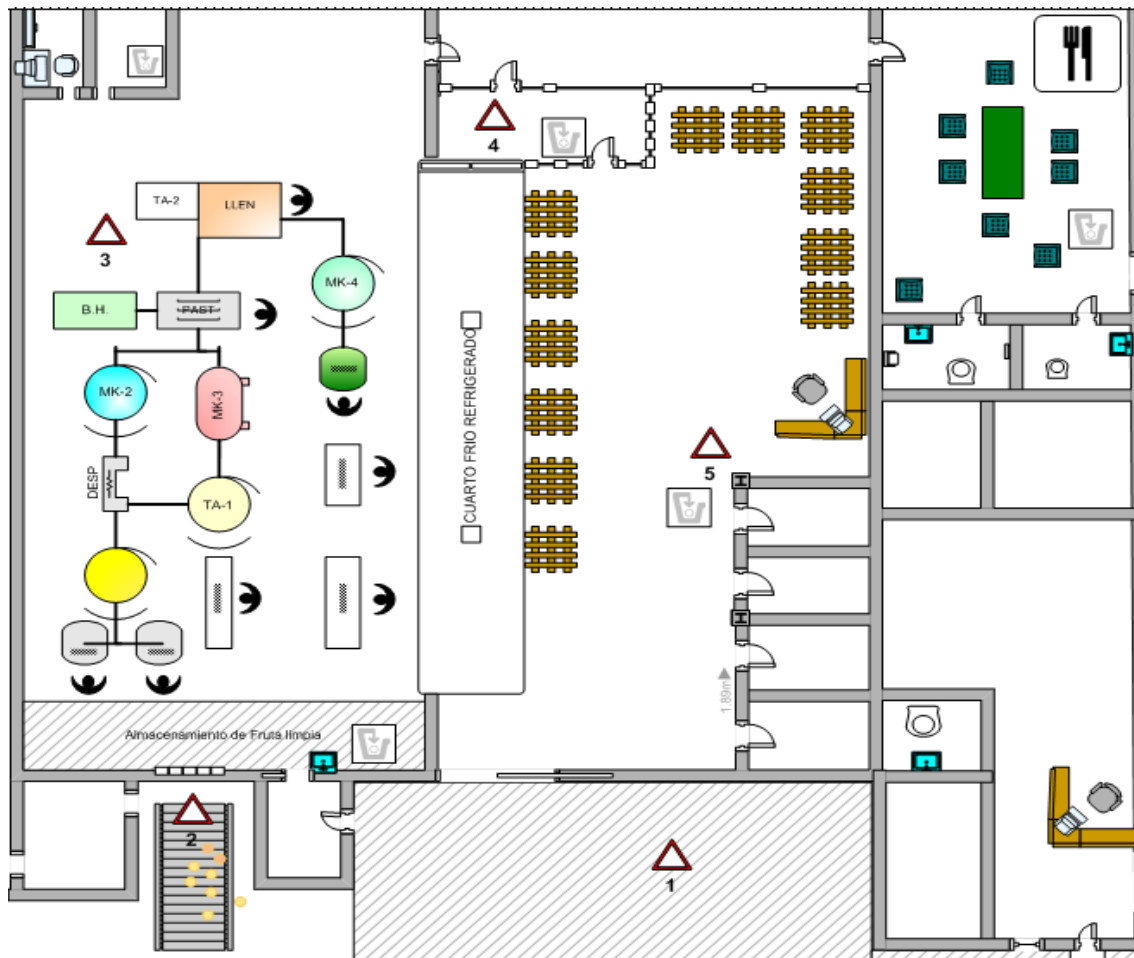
Distribución en planta de la Empresa PROJUGO
